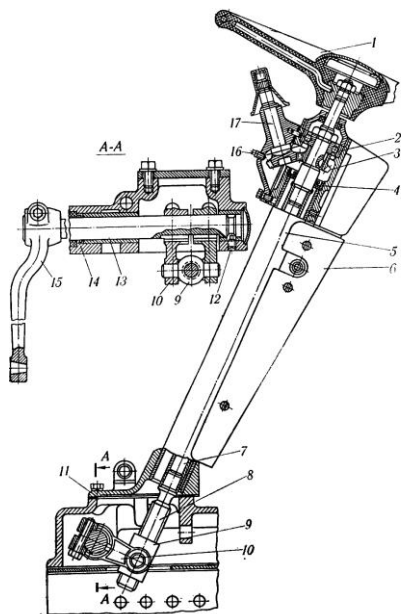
Схема рульового механізму типу гвинт-гайка (Т-40М):
